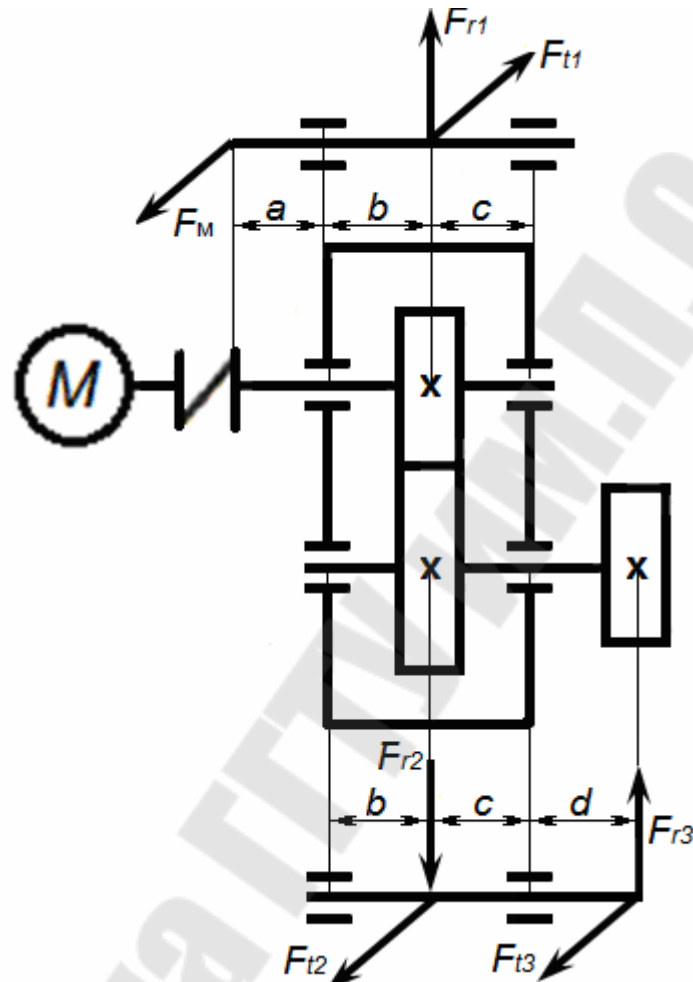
Привод конвейера с открытой цилиндрической зубчатой передачей
